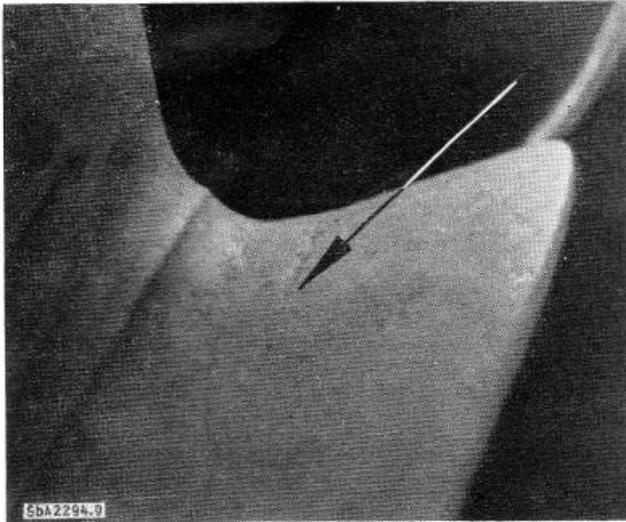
Durch Auftragschweißung ausgebesserte Umlenkrolle
